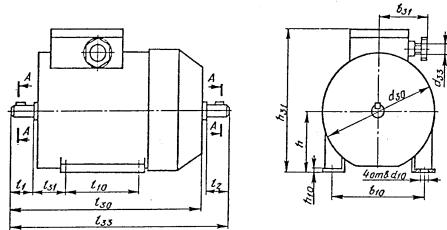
Габаритные, установочные и присоединительные размеры двигателей исполнений 1М1081, 1М1082
